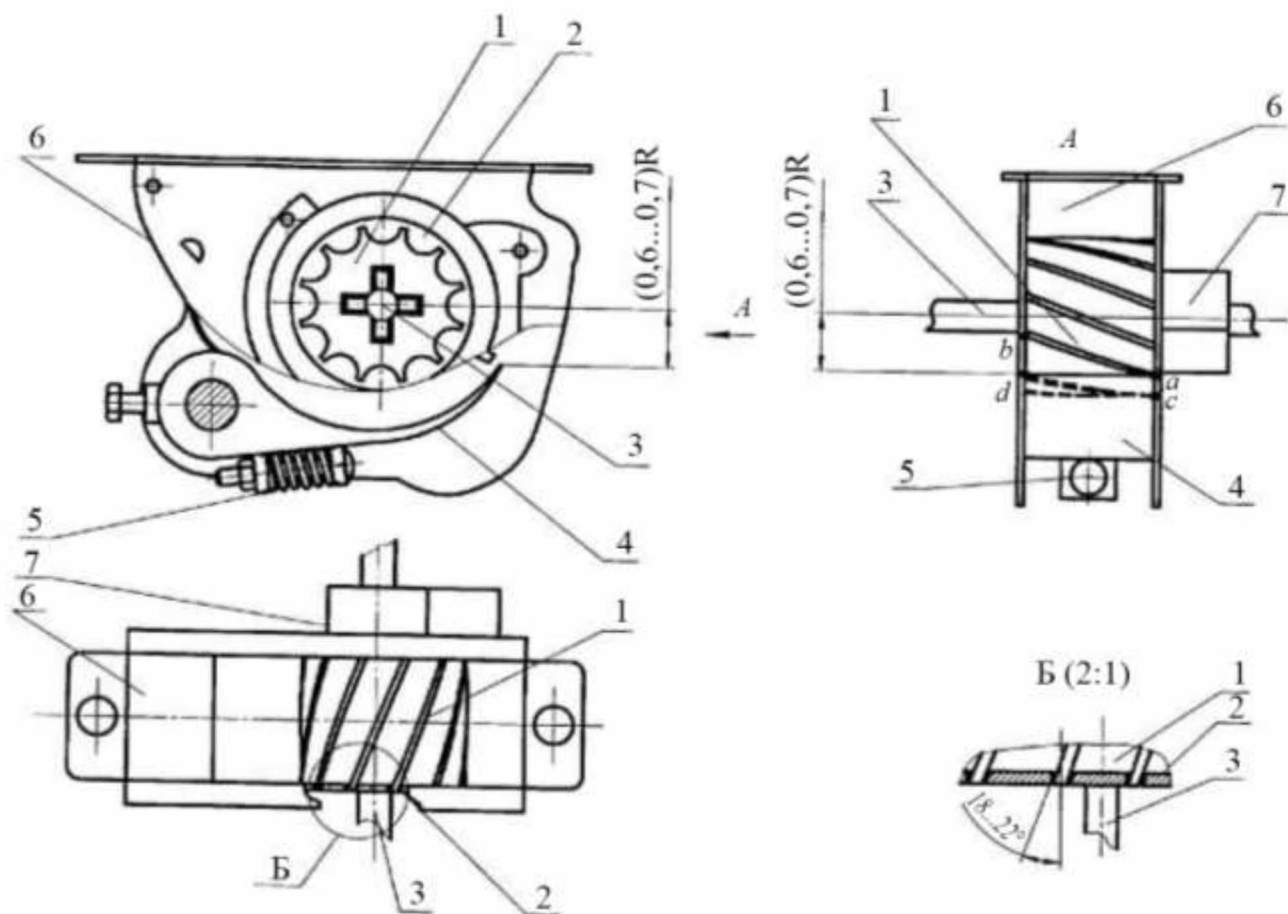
Загальний вигляд висівного апарату котушкового типу: 1 - котушка з жолобками; 2 - розетки; 3 - вал; 4 - клапан; 5-пружина; 6 - насіннева коробка; 7 - муфта
